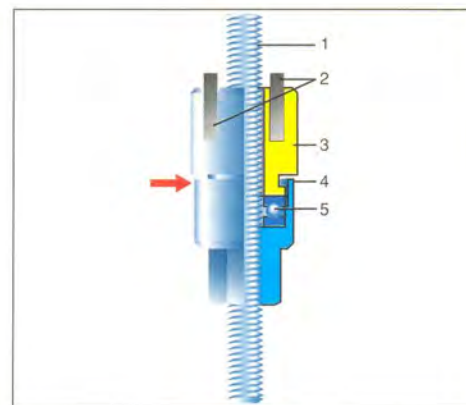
Конструкция опоры с подшипником: 1 – тяга; 2 – планка; 3 – опора; 4 – гайка; 5 – подшипник.
